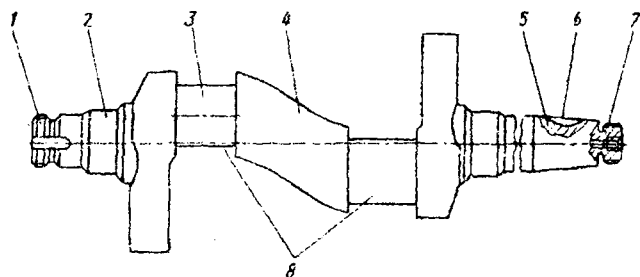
Схема расположения дефектов коленчатого вала компрессора: 1 - повреждение резьбы; 2 - изменение формы диаметрального размера, риски, задиры на коренных шейках; 3 - изменение формы диаметрального размера, риски, задиры, кольцевые выступы на шатунных шейках; 4 - искривление оси вала; 5 - изменение формы, размеров, риски, задиры на посадочной поверхности под шкив; 6 - снятие шпоночного паза; 7 - повреждение резьбы; 8 - трещины шатунных шеек
